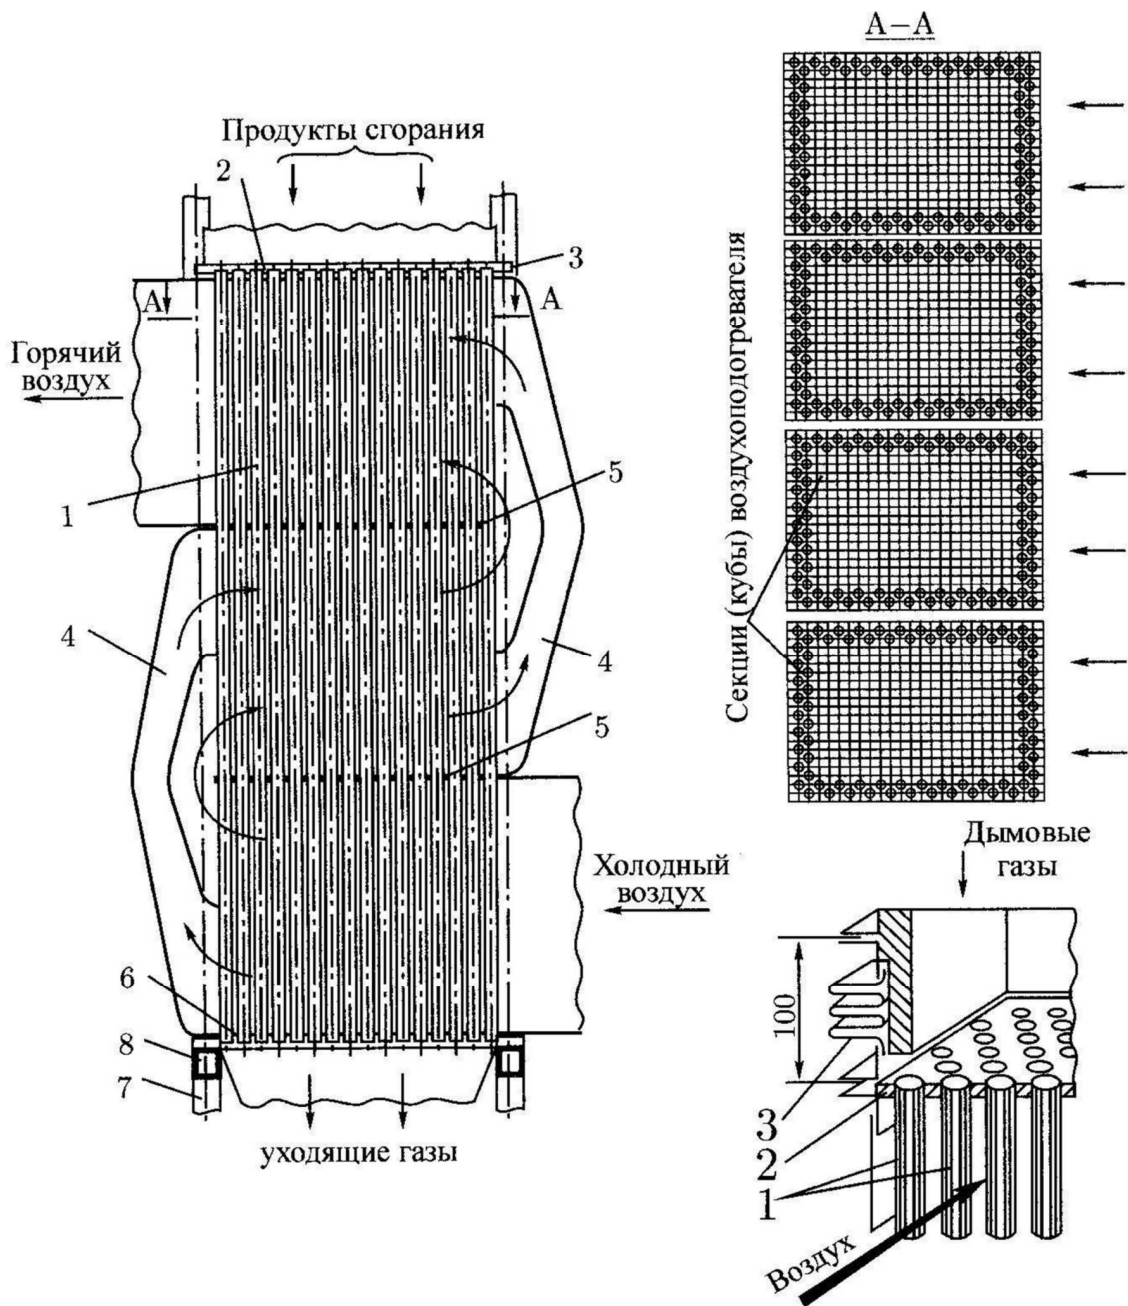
Схема регенеративного (трубчатого) воздухоподогревателя:
